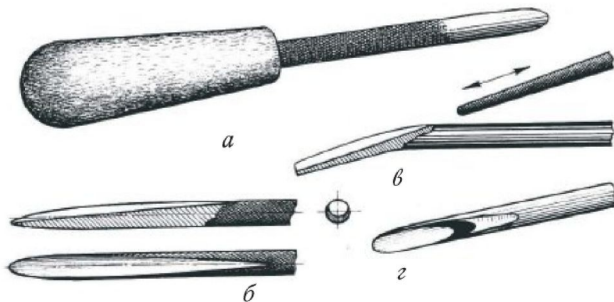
Резцы полукруглые: а) изготовленный из круглого напильника (вид на стезель с обратной стороны канавки); б) чертёж стезеля полукруглого резца; в) вытачивание канавки на изогнутом стержне (после отжига); г) изготовление из круглого стержня сверлением канала с торца
